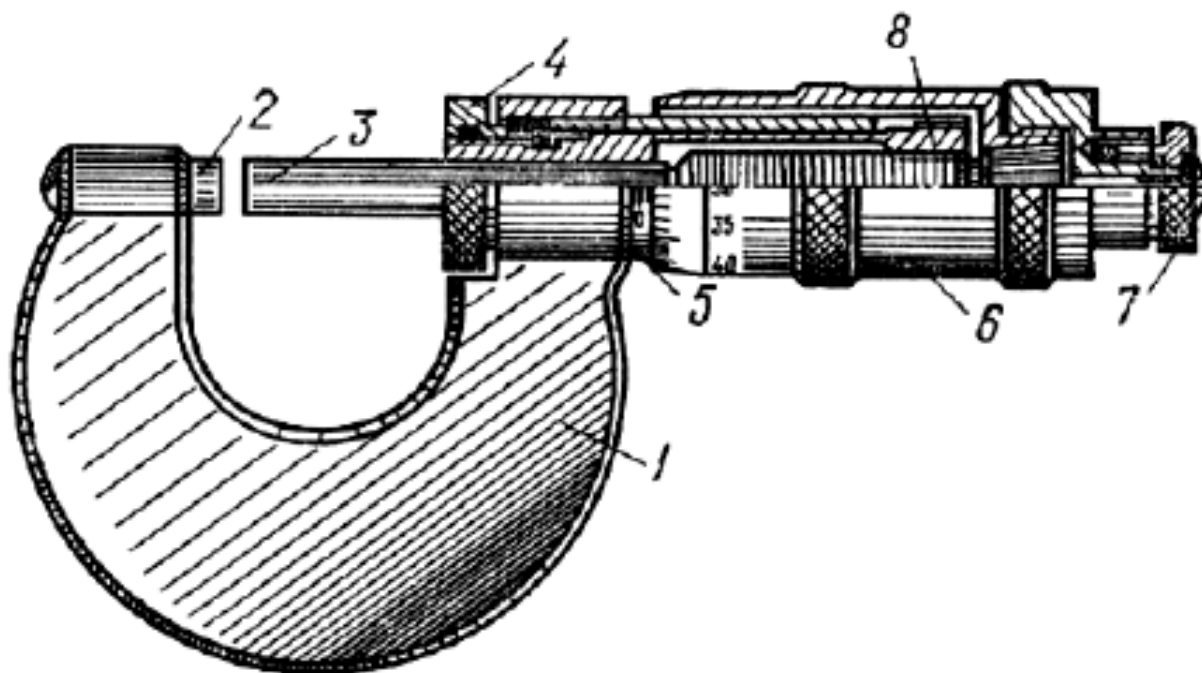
Мікрометр: 1 – скоба; 2 – п'ята; 3 – мікрометричний гвинт; 4 – регулюючий гвинт; 5 – стебло; 6 – барабан; 7 – тріскачка; 8 - гільза
